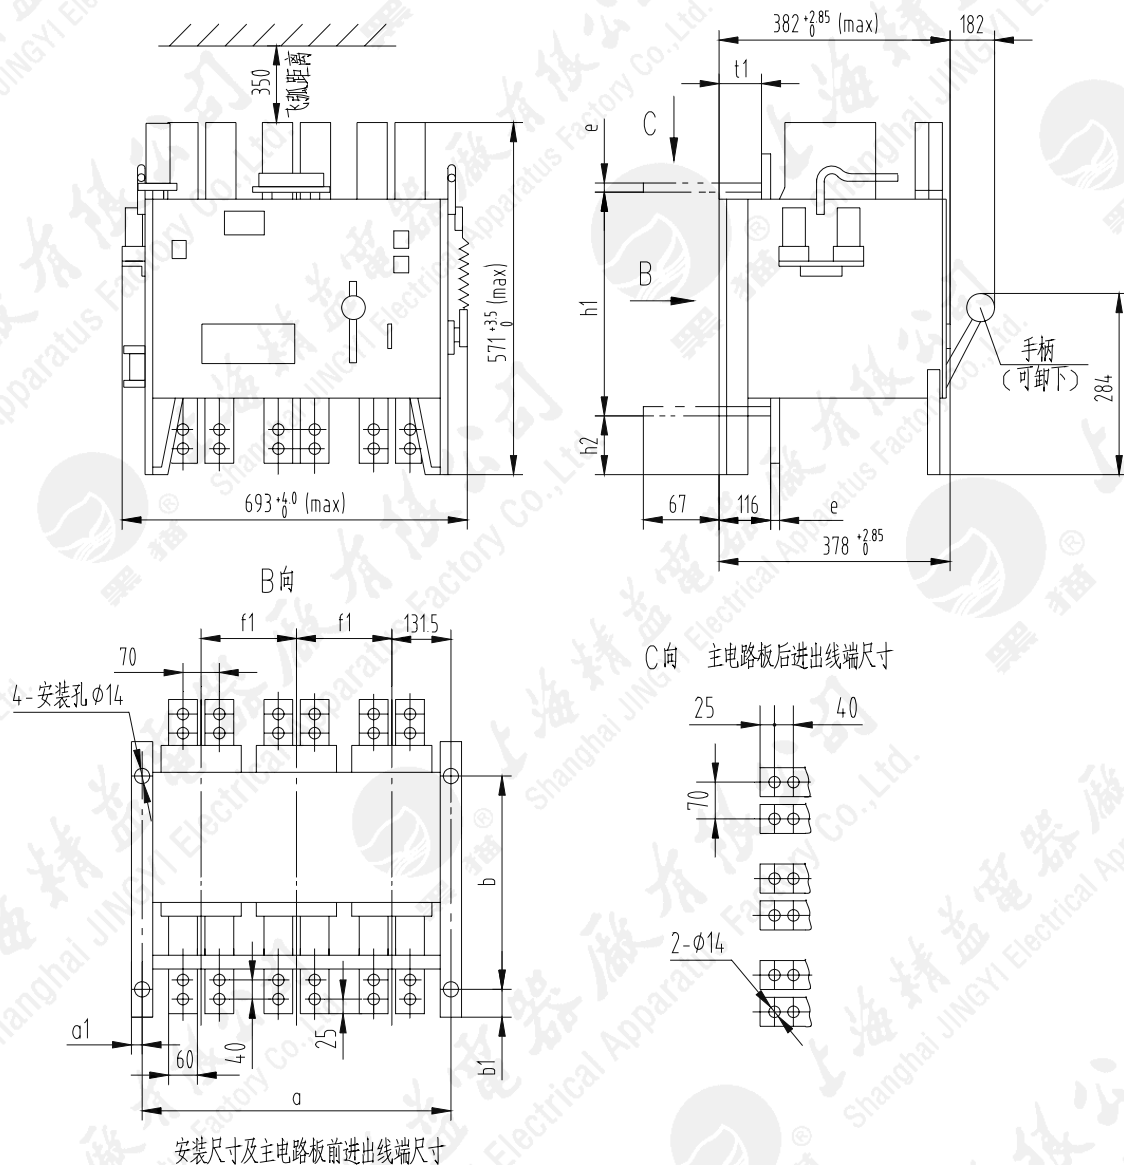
DW15-1600H 断路器的外形尺寸及安装尺寸
